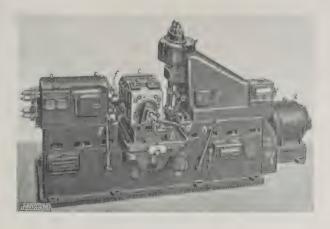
Fräsmaschine für Rippenplatten von Schieß-Defries, A.-G.
